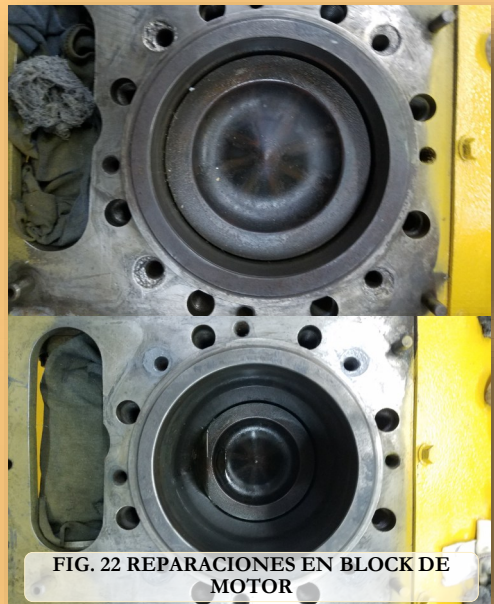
REPARACIONES EN BLOCK DE MOTOR
